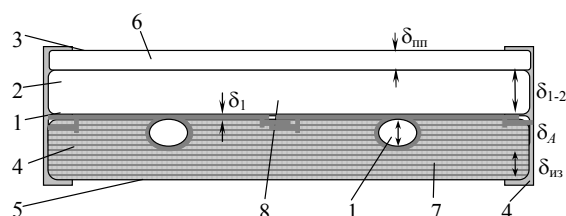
Общий вид традиционного солнечного коллектора СК-А из алюминиевого сплава: 1 — трубный регистр абсорбера; 2, 3 — коллекторные трубы; 4 — корпус СК; 5 — металлический лист; 6 — прозрачная изоляция; 7 — теплоизоляция; 8 — воздушный зазор
